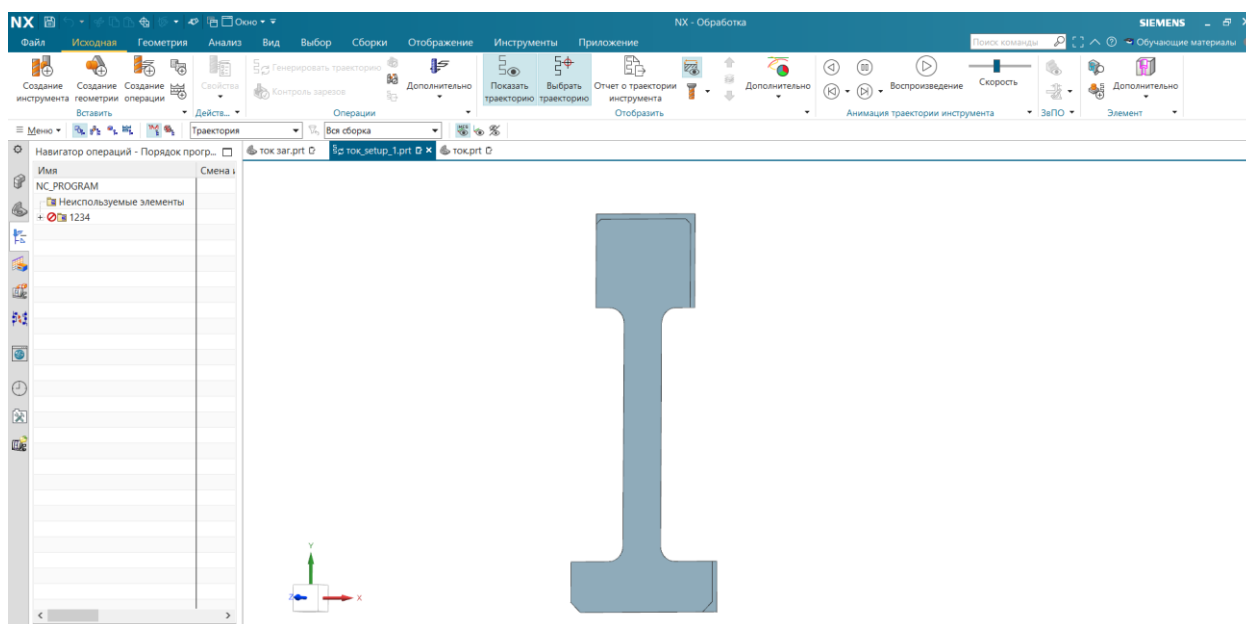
Для точіння, токарна обробка, переріз
